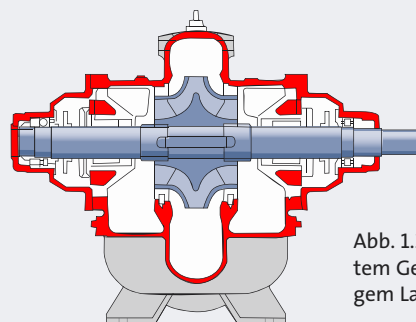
Pumpe mit geteiltem Gehäuse und zweiflutigem Laufrad
